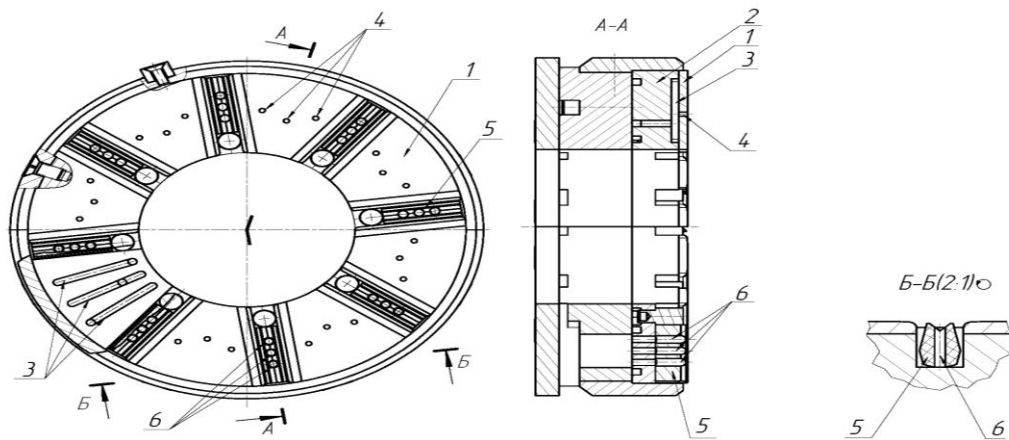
Реверсивний упорний підшипник з нереверсивними властивостями
